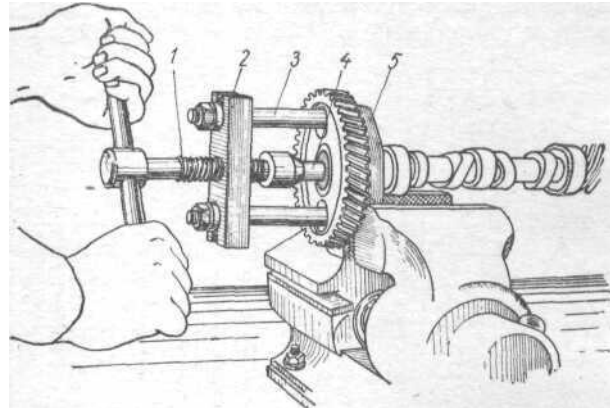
Выпрессовка шестерни распределительного вала при помощи съемника
